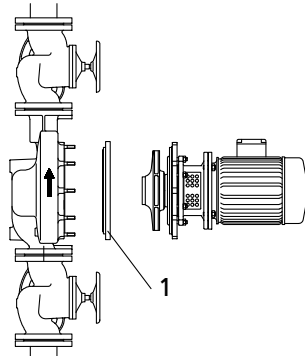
Montaggio orizzontale con flangia cieca (1 = flangia cieca, accessorio)
